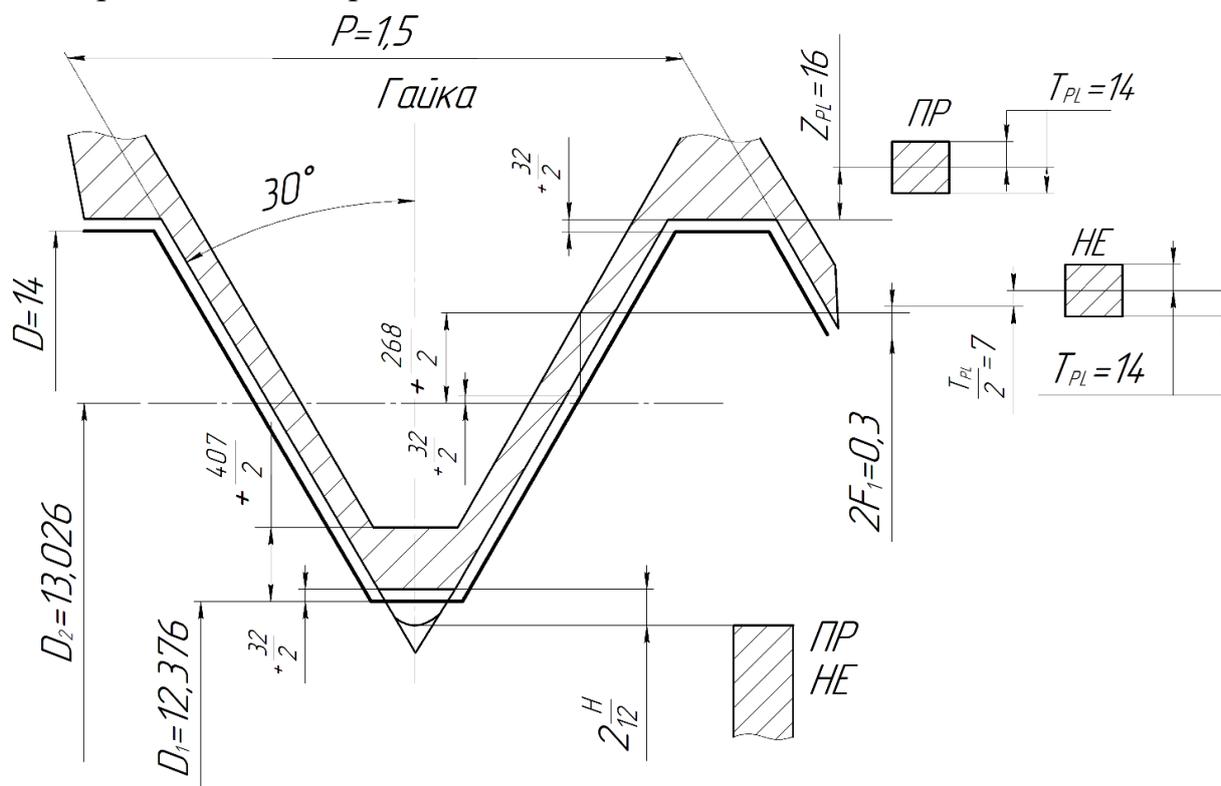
Схема расчета полей допусков резьбового калибра – пробки
